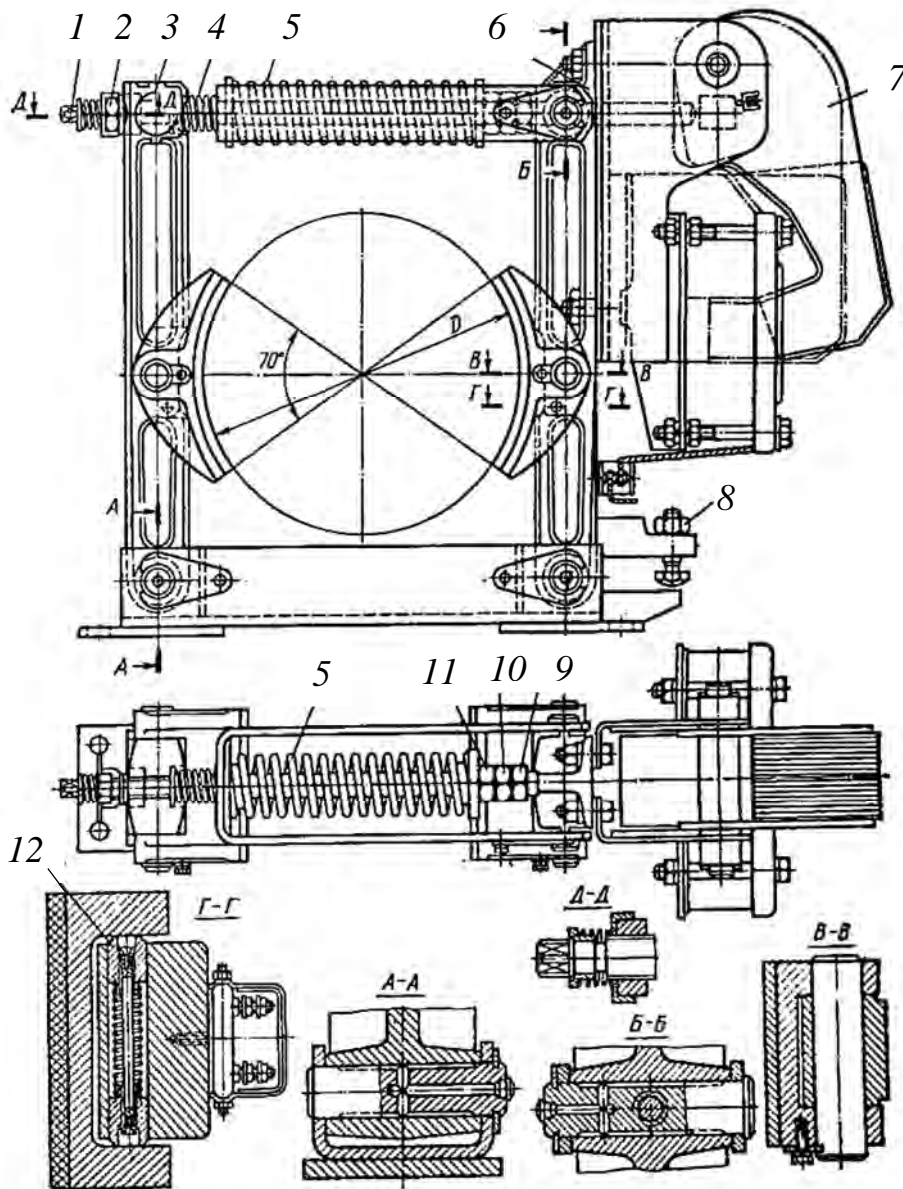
Колодочный тормоз с приводом от электромагнита: 1 – шток тормоза; 2, 9, 11 – гайки; 3 – рычаг; 4 – вспомогательная пружина; 5 – основная замыкающая пружина; 6 – тормозной рычаг; 7 – электромагнит; 8 – винт; 10 – контргайка; 12 – пружинный фиксатор
